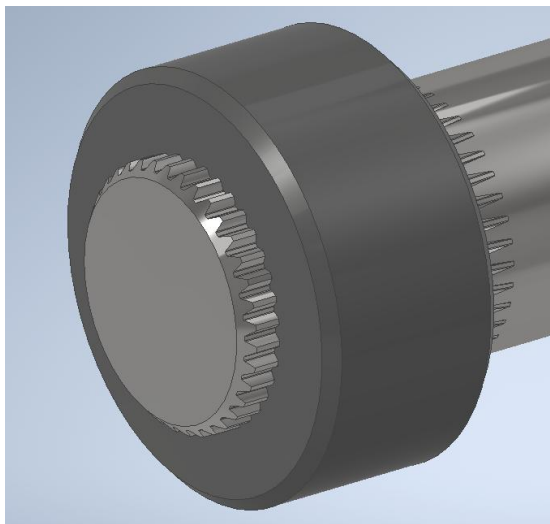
Шліцьове з'єднання з евольвентними шліцями Involute Splines
